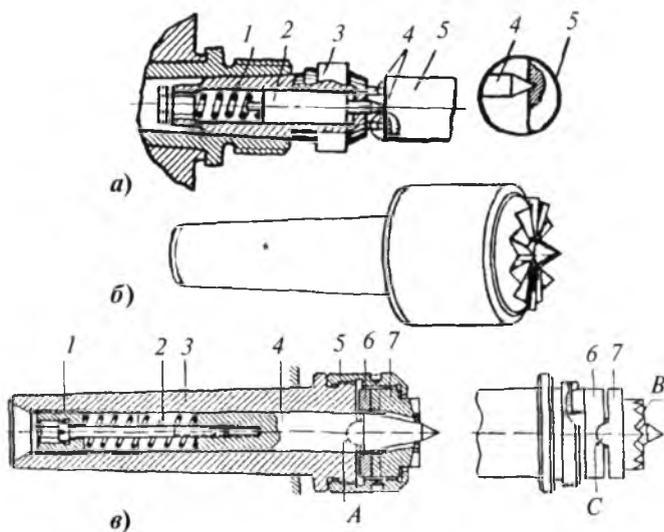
Центра: а — плавающий: 1 — пружина; 2 — плавающий центр; 3 — корпус-гайка; 4 — жесткие опоры; 5 — деталь; б — рифленный; в — грибовый: 1 — опорная втулка; 2 — пружина; 3 — корпус; 4 — центр; 5 — гайка; 6 — шайба; 7 — сменная опора; А — сфера; В — рифленая поверхность; С — опора сферическая
